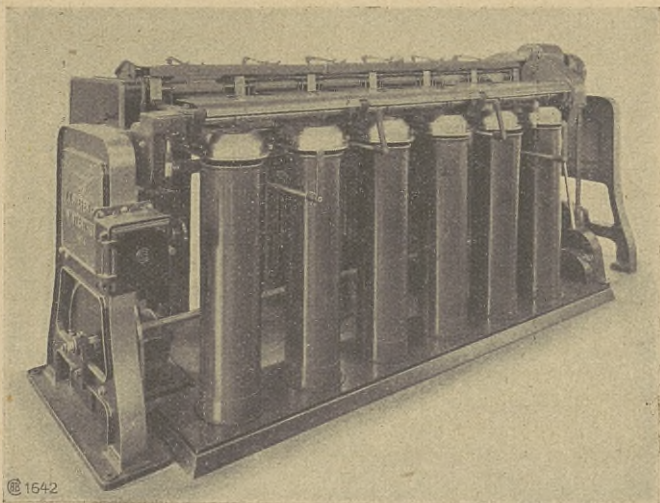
Elektrischer Einzelantrieb einer Streckmaschine.
